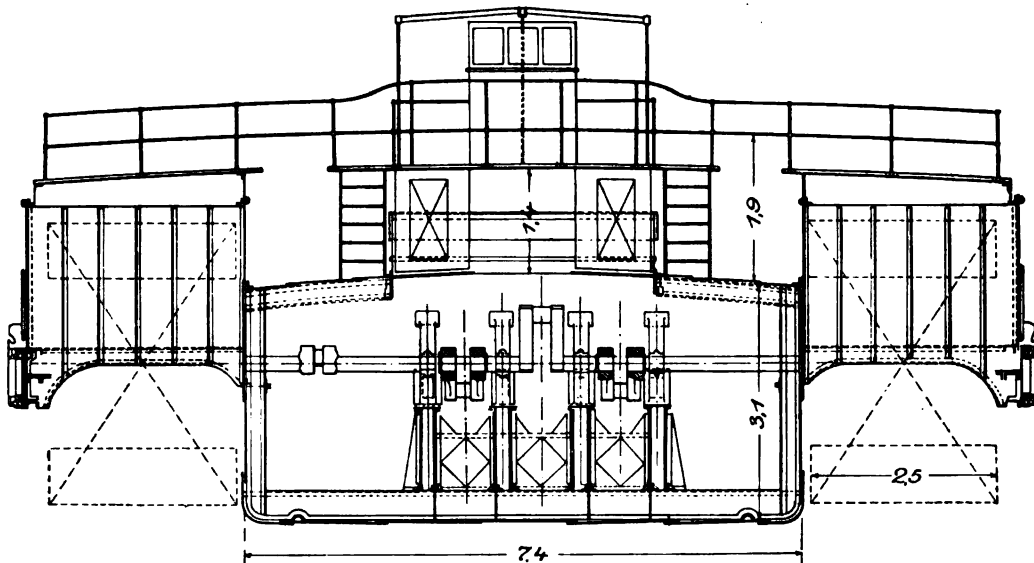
Güterdampfer mit Seitenrädern, Querschnitt 1 : 100.
